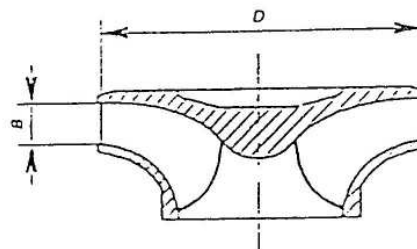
Dimensiones principales del rodete/impulsor de máquinas radiales
